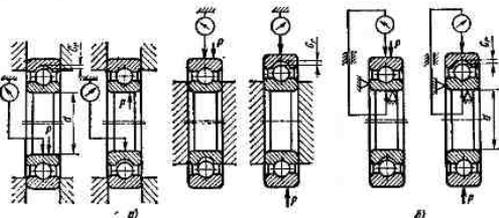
Схема измерения радиального зазора: а — с креплением колец по торцу; б — без крепления колец;  $G_r$  — радиальный зазор;  $P$  — измерительная нагрузка
